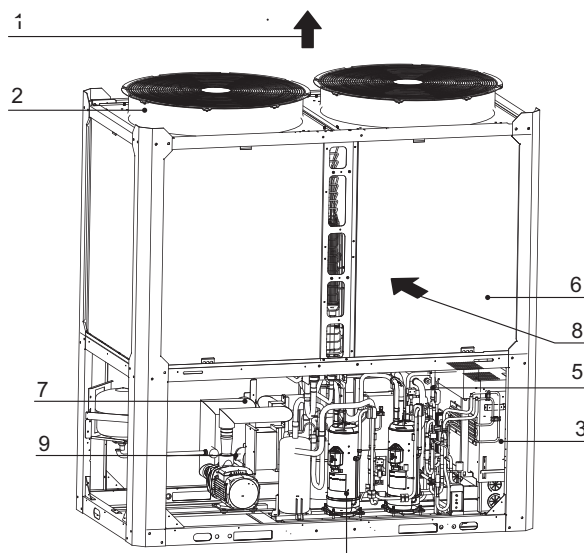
Partes principais do MC SU90M-RN8L-B
